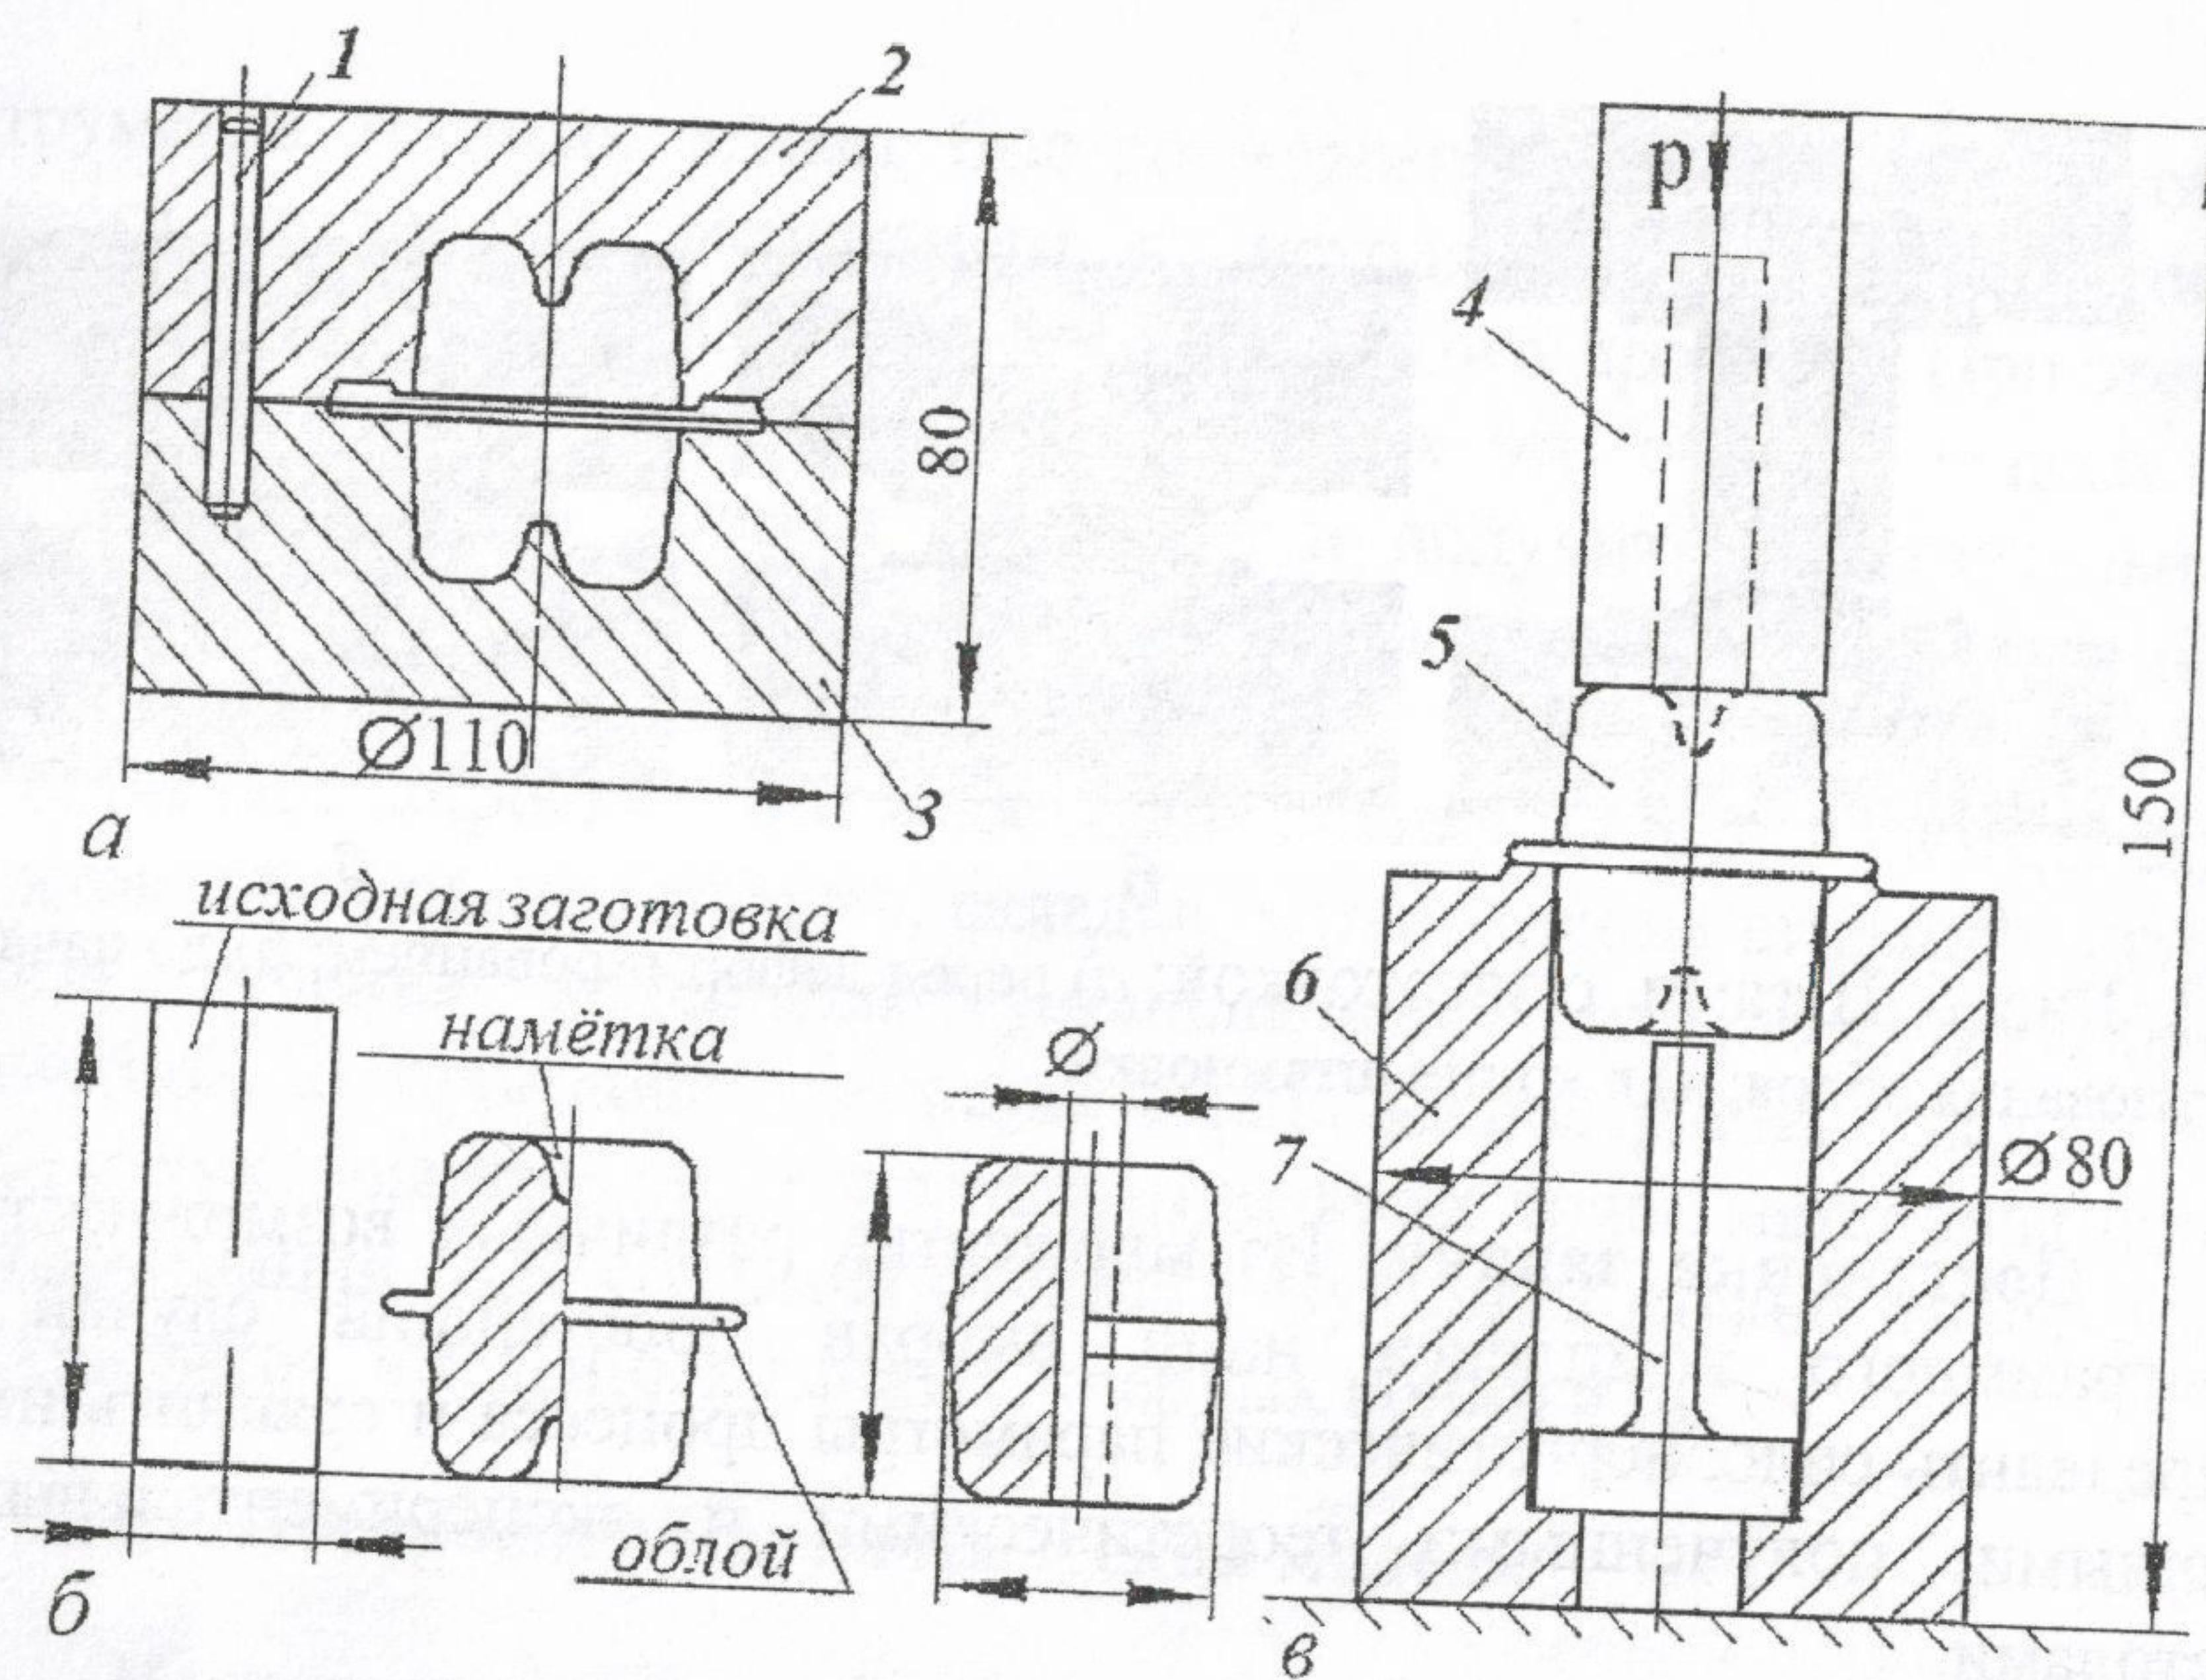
Конструкция штампов для объемной штамповки (а) и просечного штампа (в), поковка (б): 1 – направляющие; 2,3 – верхний и нижний штампы; 4 – пuhanсон; 5 – поковка; 6 – матрица; 7 – просечка
